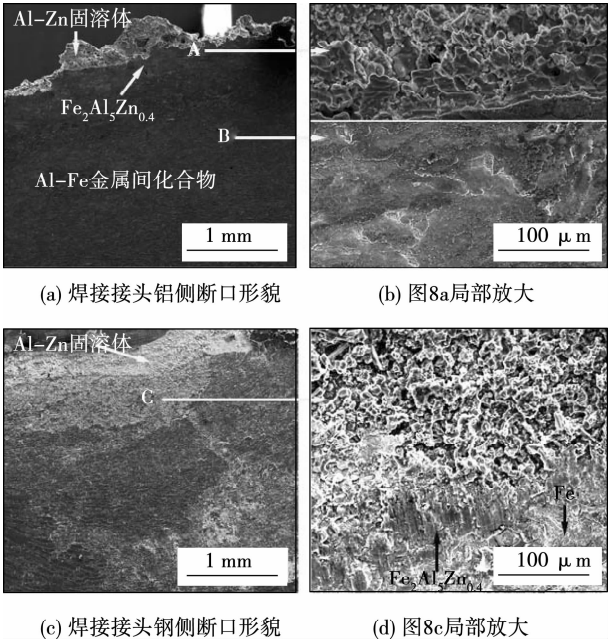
Al-Mg 焊丝焊接接头断口形貌
